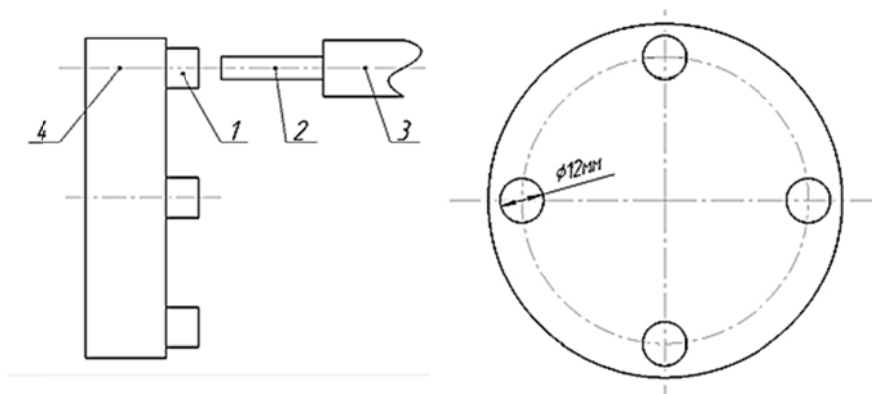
Шлифовальный круг в сборе (1 – абразивная головка; 2 – заготовка ; 3 – устьево крепления заготовки; 4 – шлифовальный круг)
